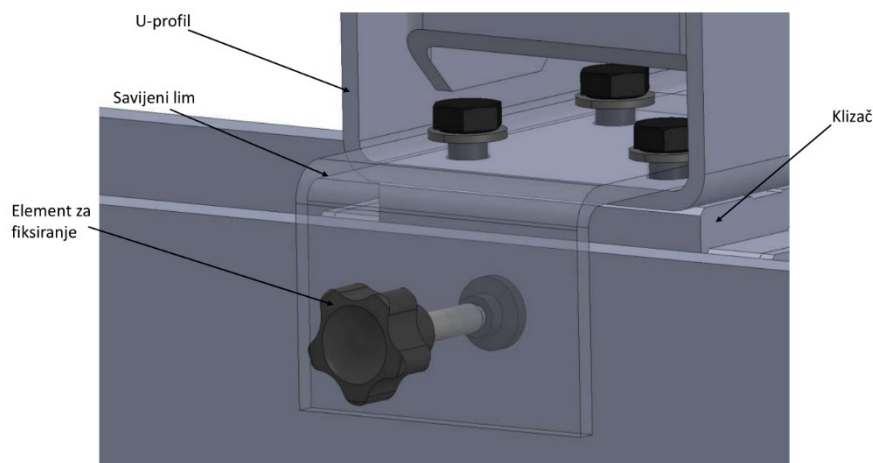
Dimenzije elementa za fiksiranje stupova [23]
